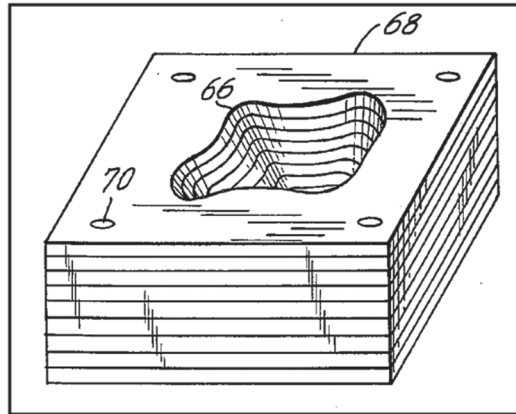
Molde fabricado com a técnica de adição de camadas por DiMatteo [8].
